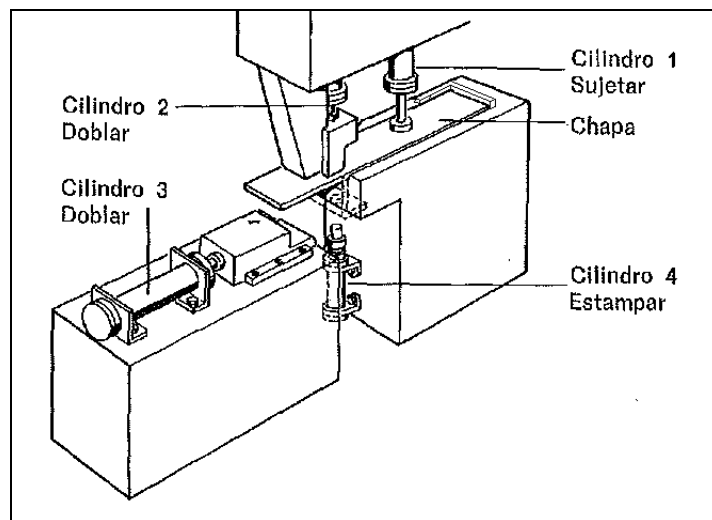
66 - Croquis para máquina de doblado y estampado.
